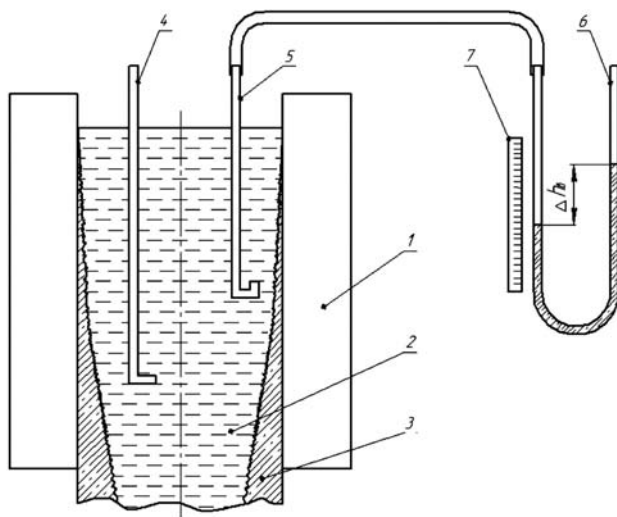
Схема пристрою для фіксації руху розплаву в рідкій лунці. 1 – кристалізатор, 2 – розплав, 3 – затверділа кірка заготовки, 4 і 5 – вимірювальні трубки, 6 – водяний манометр, 7 – шкала вимірювань.
